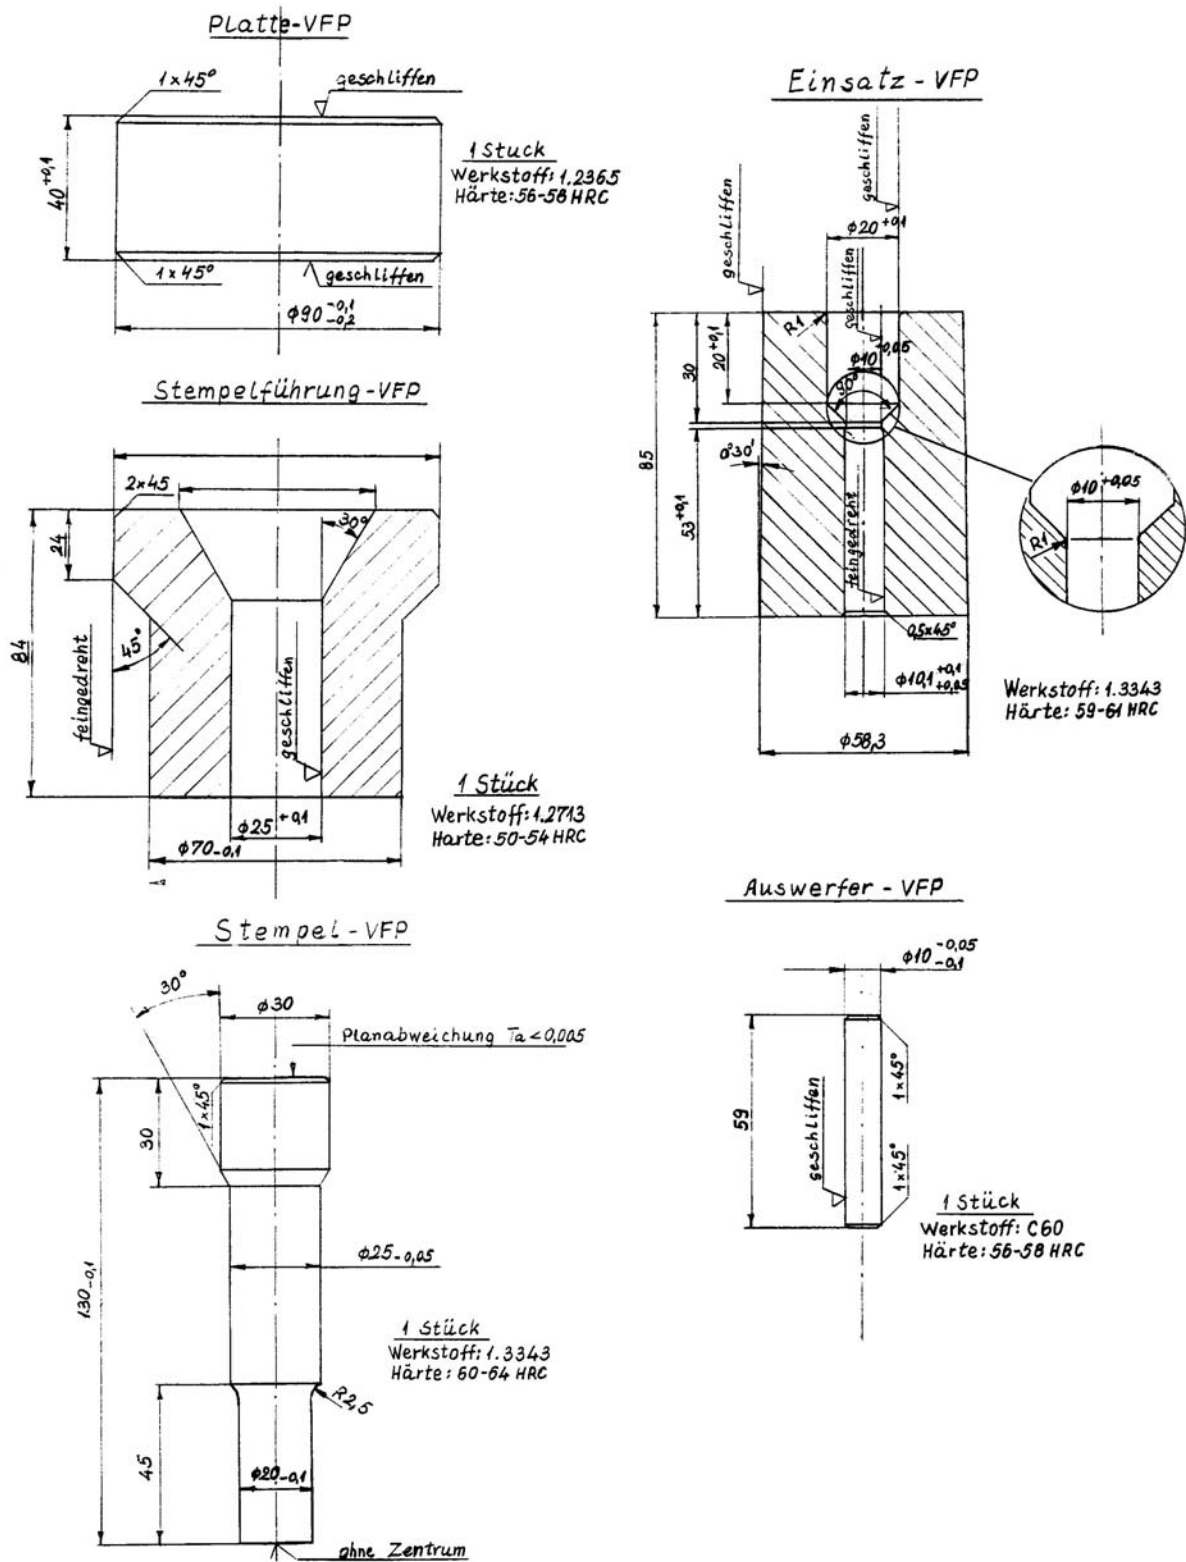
Werkzeuge für das Vorwärtsfließpressen
